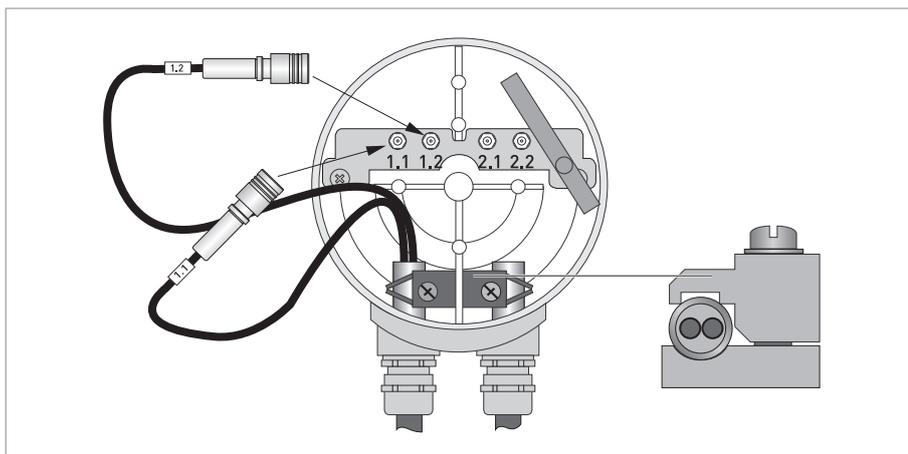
Conecte los cables en la caja de conexión del sensor de caudal
